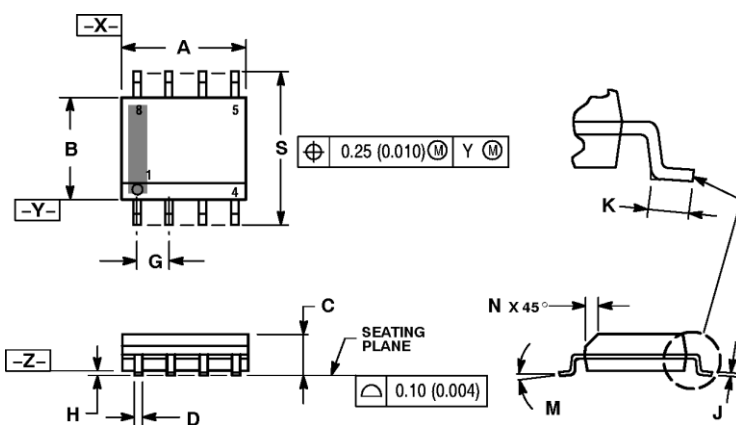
Внешний вид корпуса SOIC-8.
